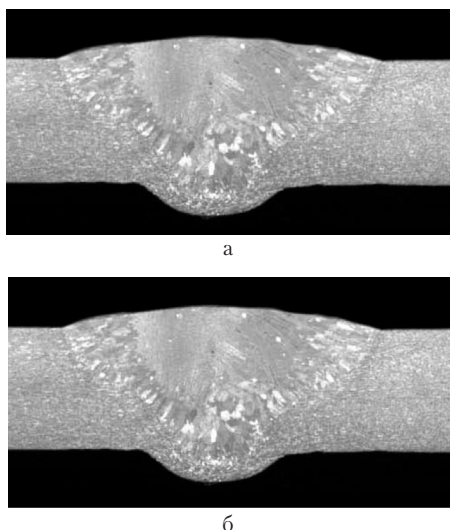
Сварные соединения листов толщиной 6,0 мм сплава АМг6, полученных свободно расширяющейся дугой (а) при скорости сварки 20 см/мин и сжатой дугой (б) при скорости сварки 40 см/мин
